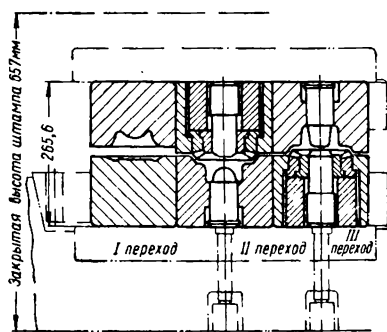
Схема штамповки шестерни с оформлением зубьев в предварительном и окончательном переходах
